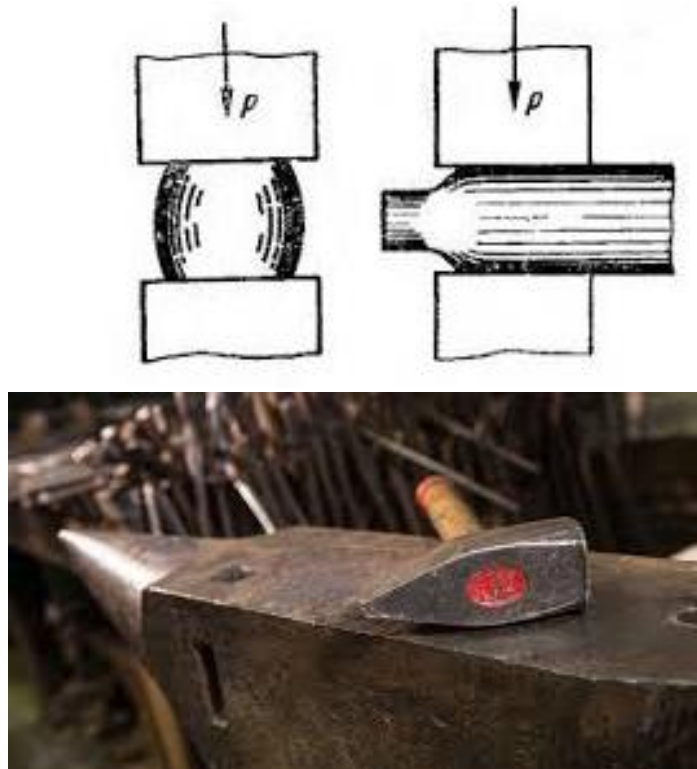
Схема операцій ручного кування (а); інструменти для проведення ручного кування (ковадло і молот)
